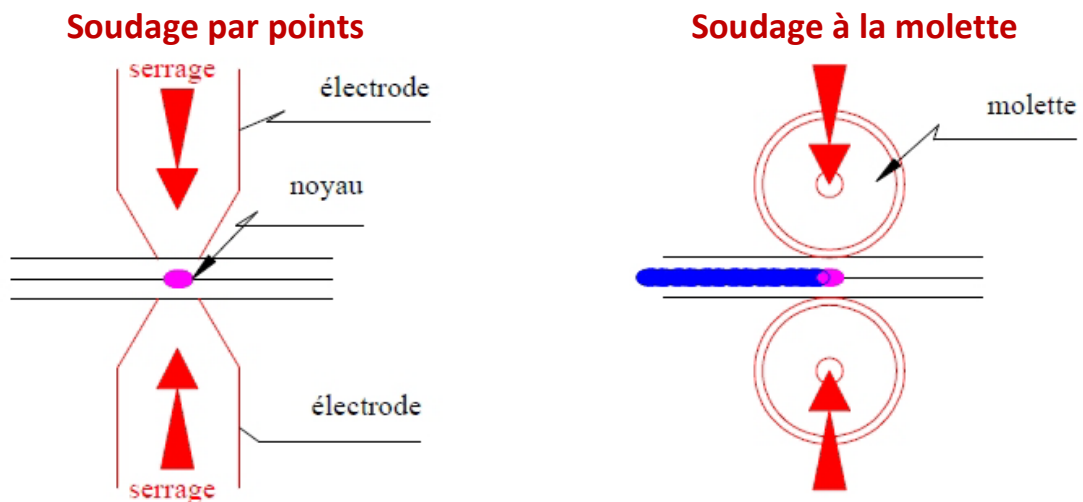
Procèdes de soudage pression et fusion [9].
